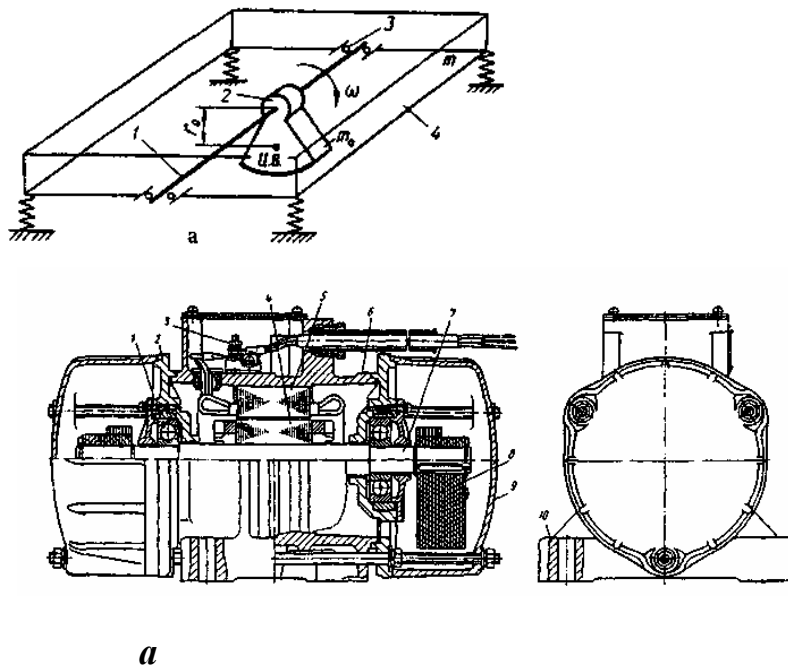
Дебалансний відцентровий вібратор: а- схема; б- конструкція.
